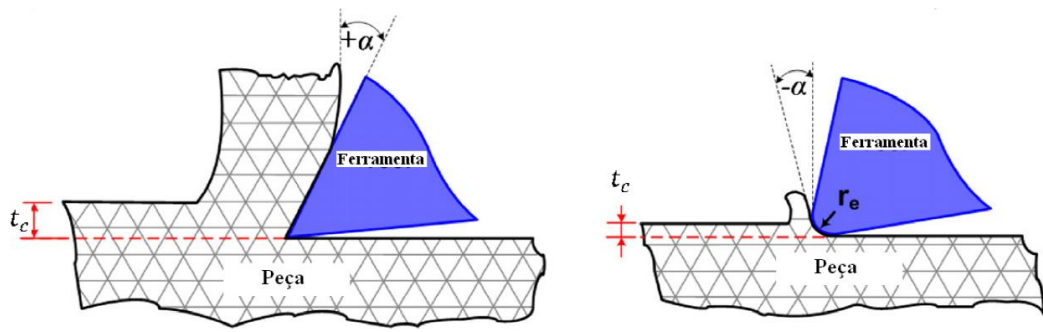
Macro maquinagem (esquerda) e micro maquinagem (direita).[31]
